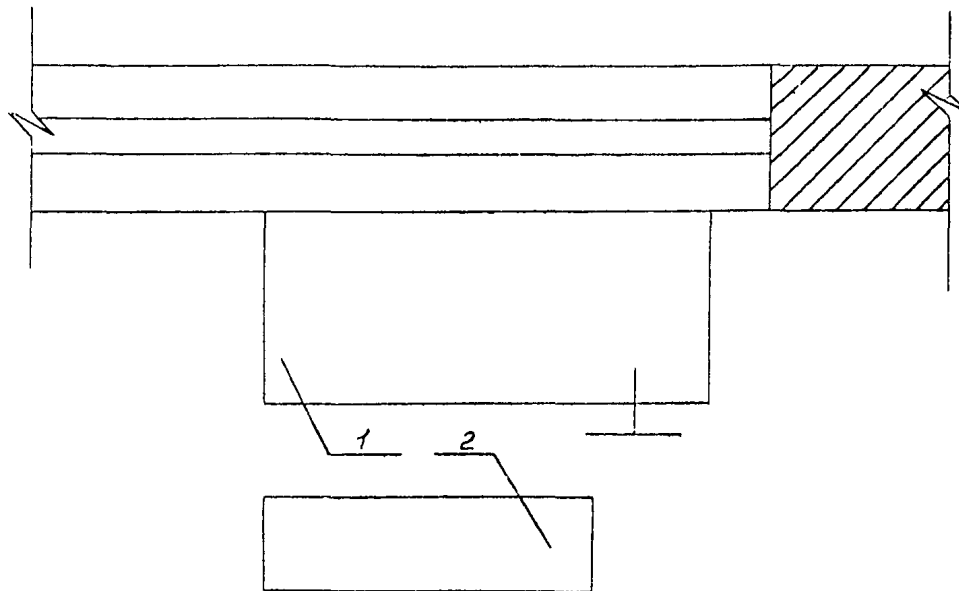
Типовая схема планировки рабочего места разборки и сборки карданных валов
